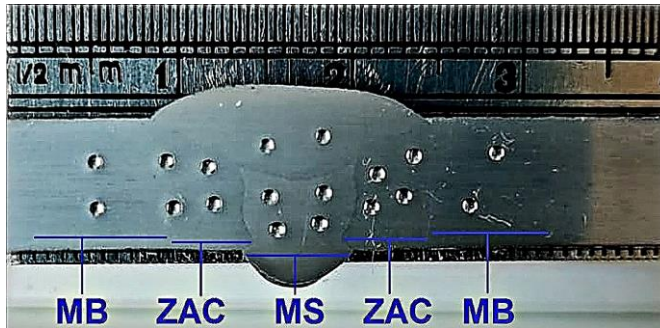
Indentaciones de dureza HRB realizadas por cada zona de la junta soldada.
